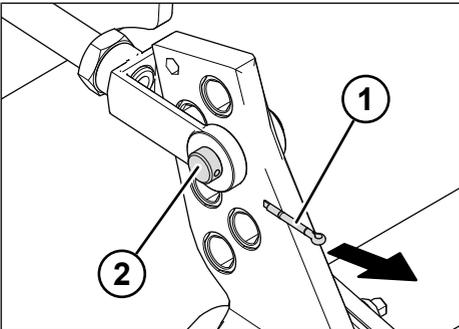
Retirar el bulón del cabezal de la horquilla
